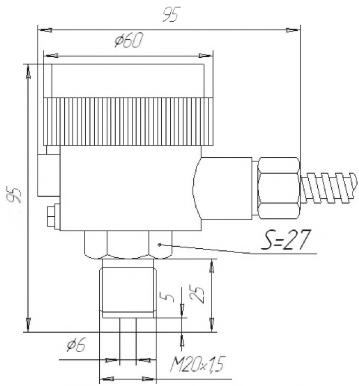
Модель 1190. Взрывонепроницаемая оболочка, нержавеющий корпус, встроенный кабель.
